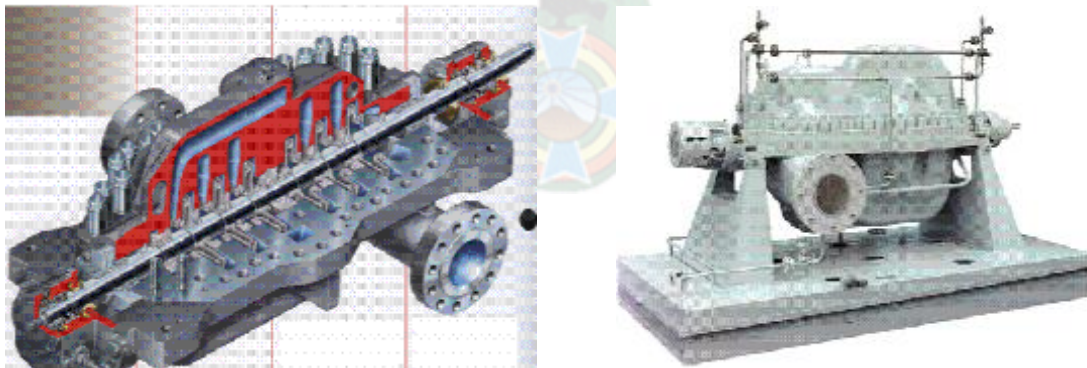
Bomba multietapa de voluta axialmente partida, impulsores entre cojinetes.
